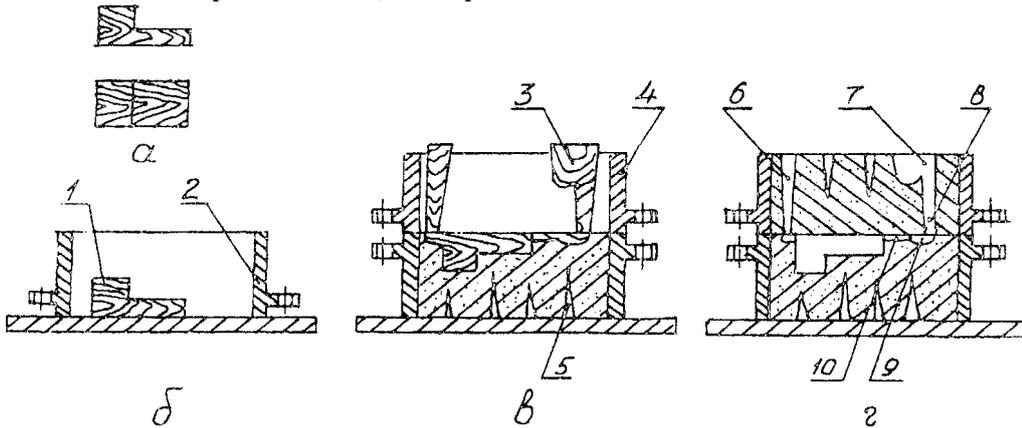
Последовательность операций при формовке в двух опоках по неразъемной модели: а-модель отливки, б, в - изготовление нижней и верхней полуформ, г-форма в сборе; 1-модель отливки, 2-нижняя опока, 3-модель литниковой системы, 4-верхняя опока, 5-вентиляционные каналы, 6-выпор, 7-литниковая чаша, 8-стояк, 9-шлакоуловитель, 10-питатели
